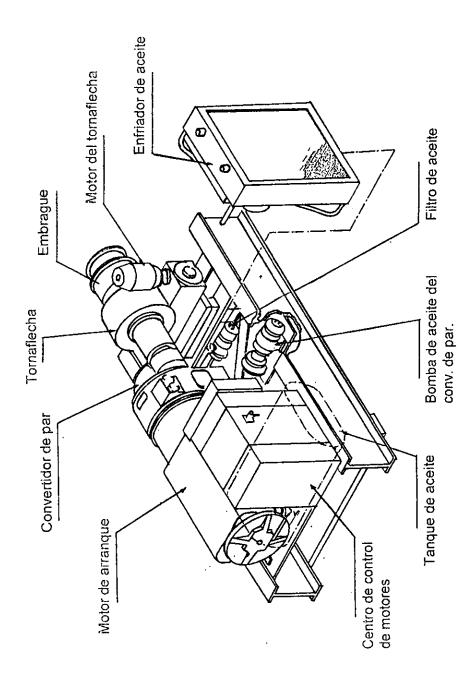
Equipo Auxiliar - Turbina de gas W 501 - D
